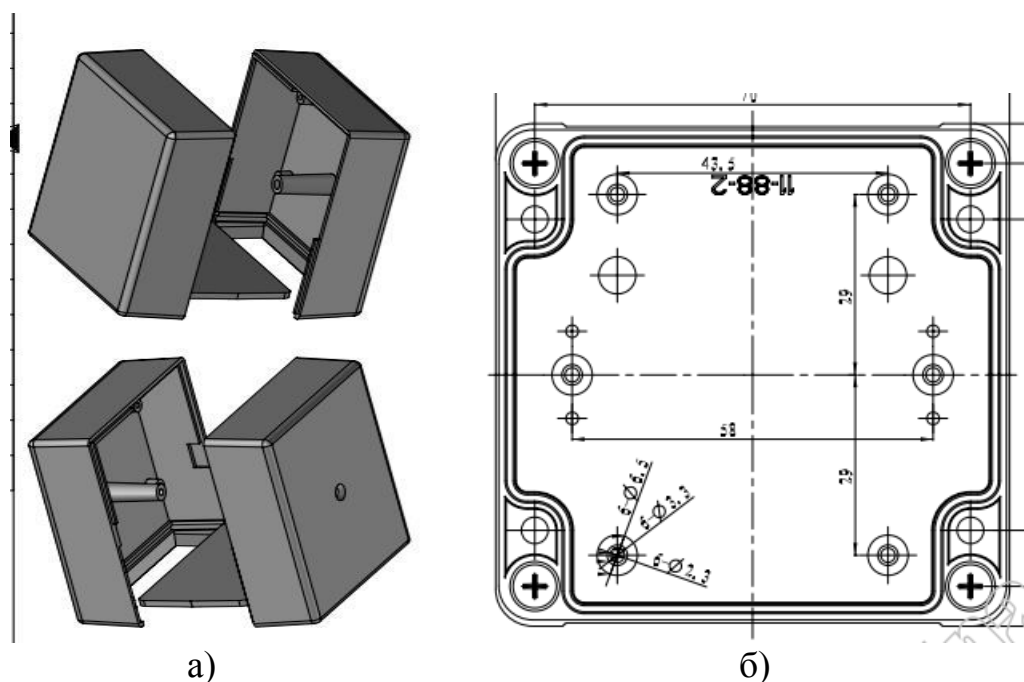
Недостатки корпусов а) Kradex Z60, б) 11-88
